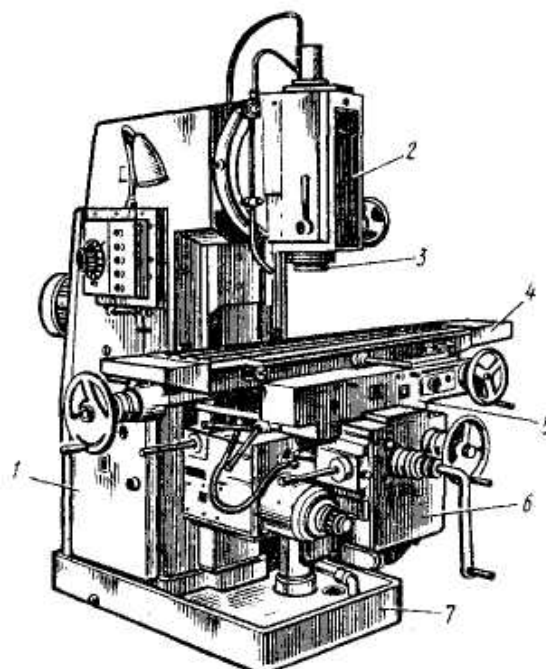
Вертикально-фрезерный станок: 1 – станина; 2 – шпиндельная головка; 3 – шпиндель; 4 – стол; 5 – каретка; 6 – консоль; 7 – фундаментная плита
